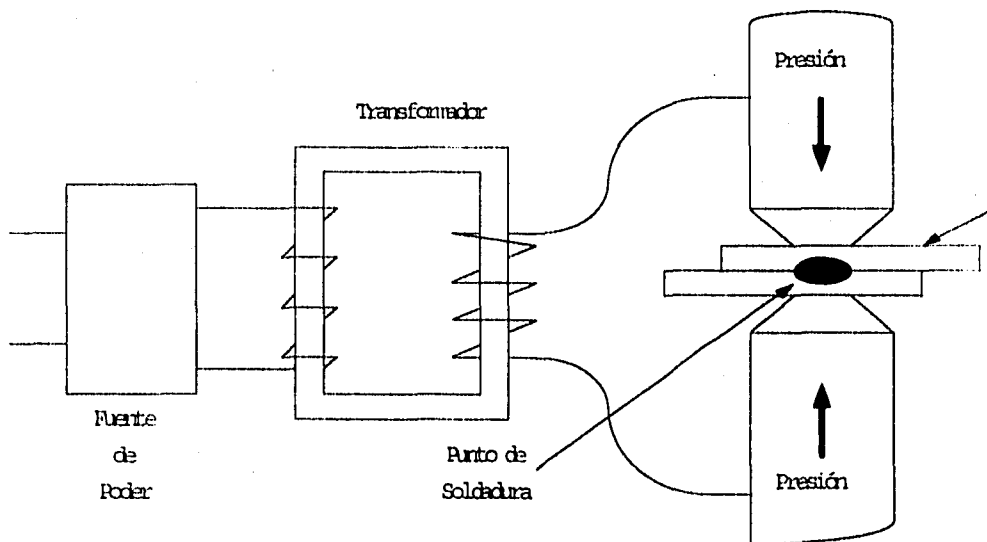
Diagrama esquemático del proceso de soldadura a presión.
